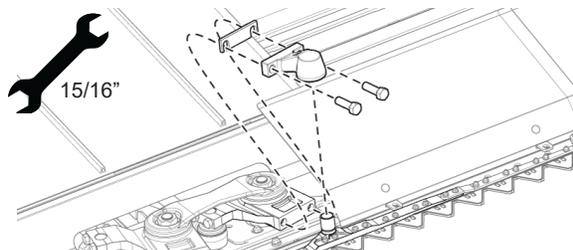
Desmonte el cojinete izquierdo de la cabeza de la cuchilla
